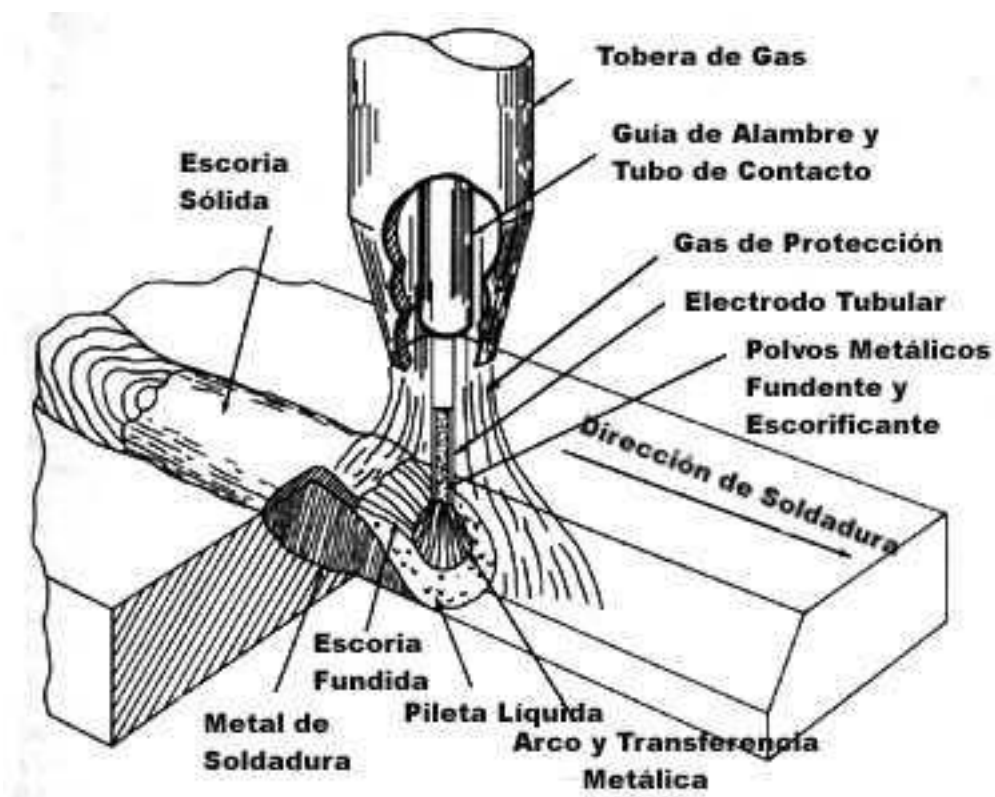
Soldadura por arco con núcleo de material fundente (FCAW)
